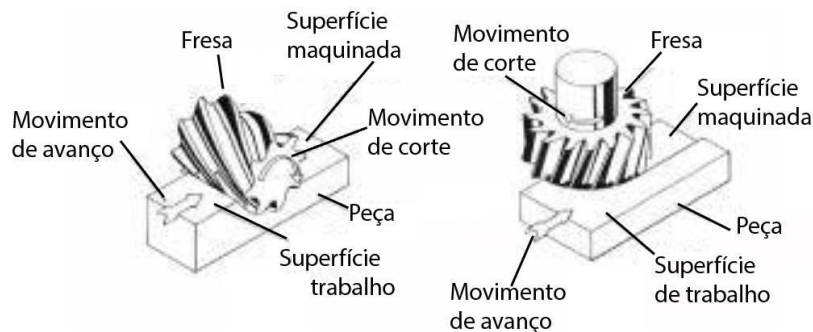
Fresagem de topo e fresagem cilíndrica
